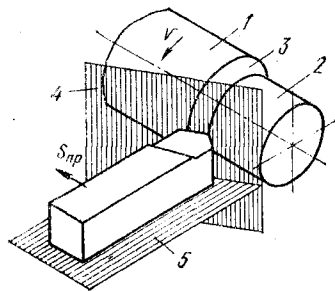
Координатные плоскости и поверхности обрабатываемой заготовки
